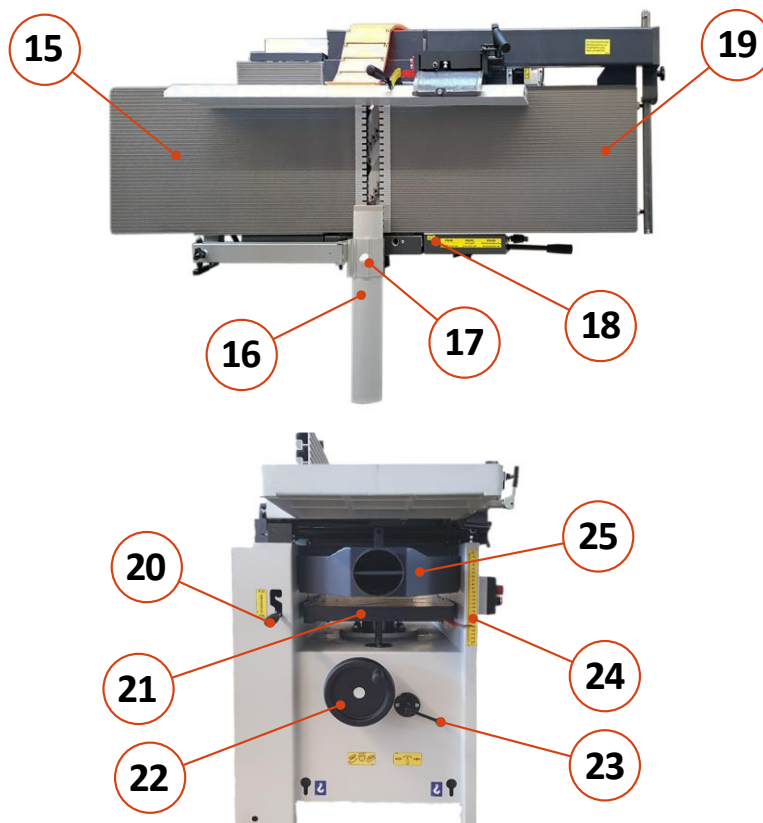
Maschinenübersicht - Hauptkomponenten 2
